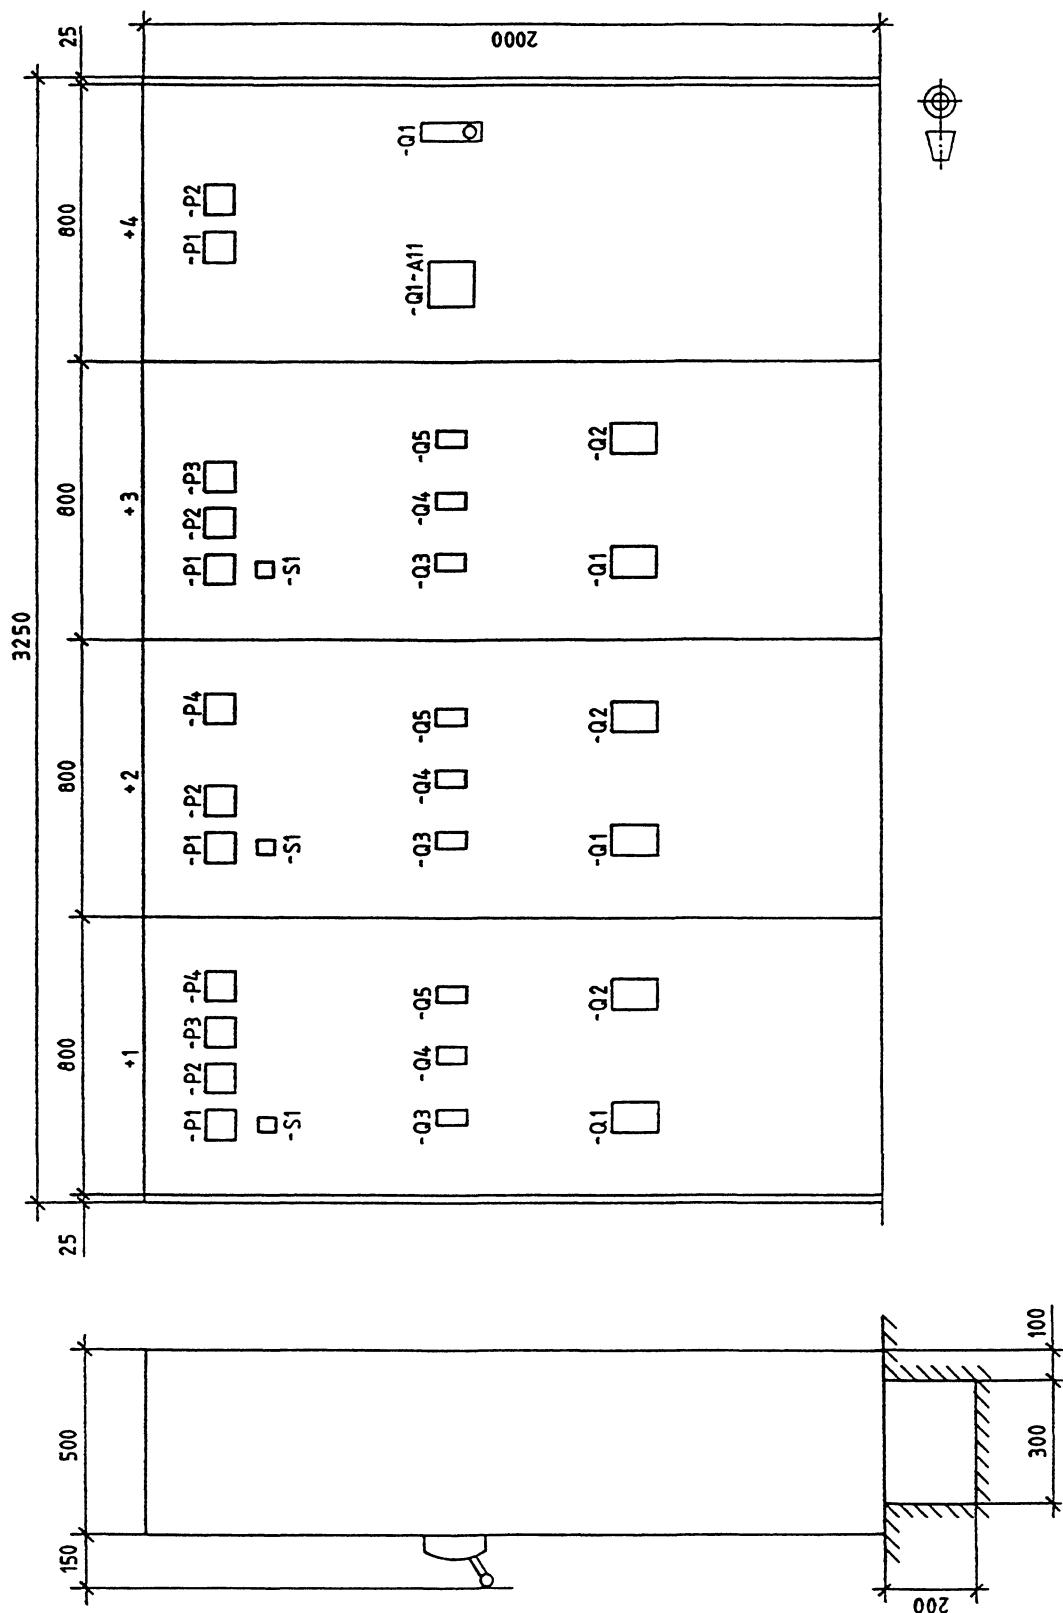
Exemple de dessin de disposition; ensemble d'appareillage +A sur la figure 25.
